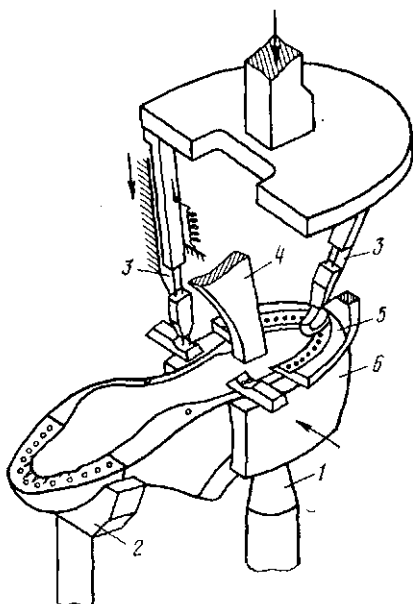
Схема исполнительных органов полуавтомата для затяжки пяточной части заготовки верха обуви
